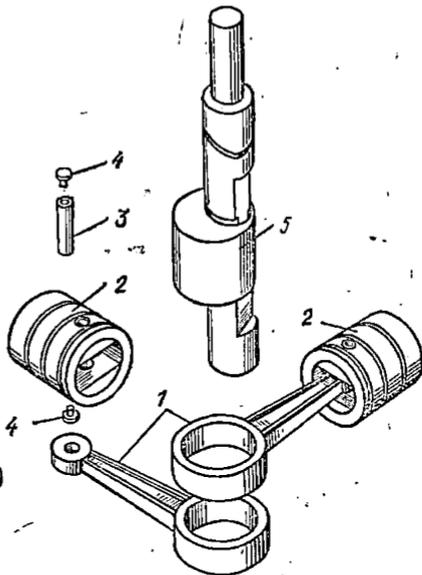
Механизм движения компрессора ФГО,7 ~ 3:
